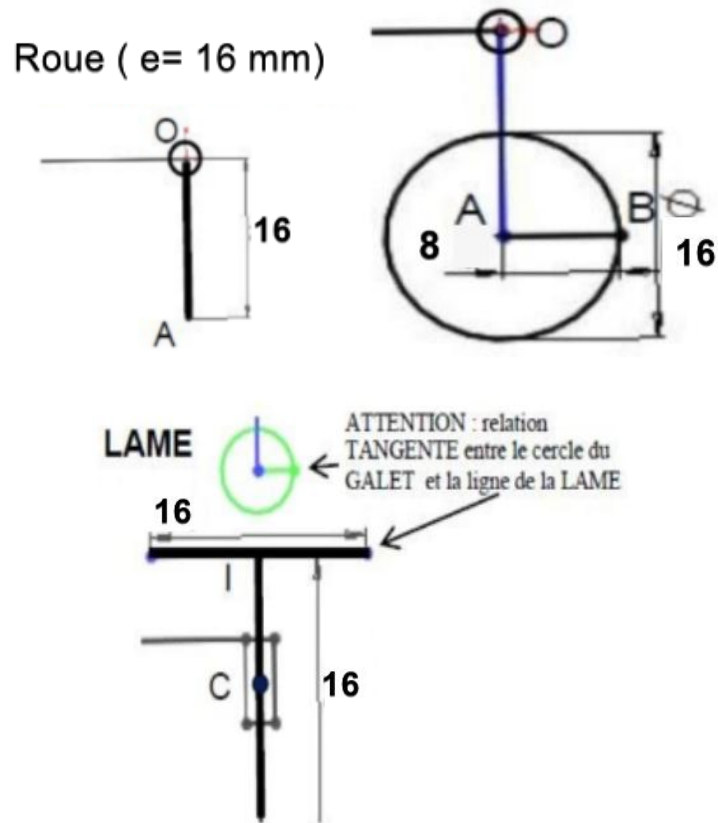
Dimension de (Roue - Roue Connecteur - Porte lame)
